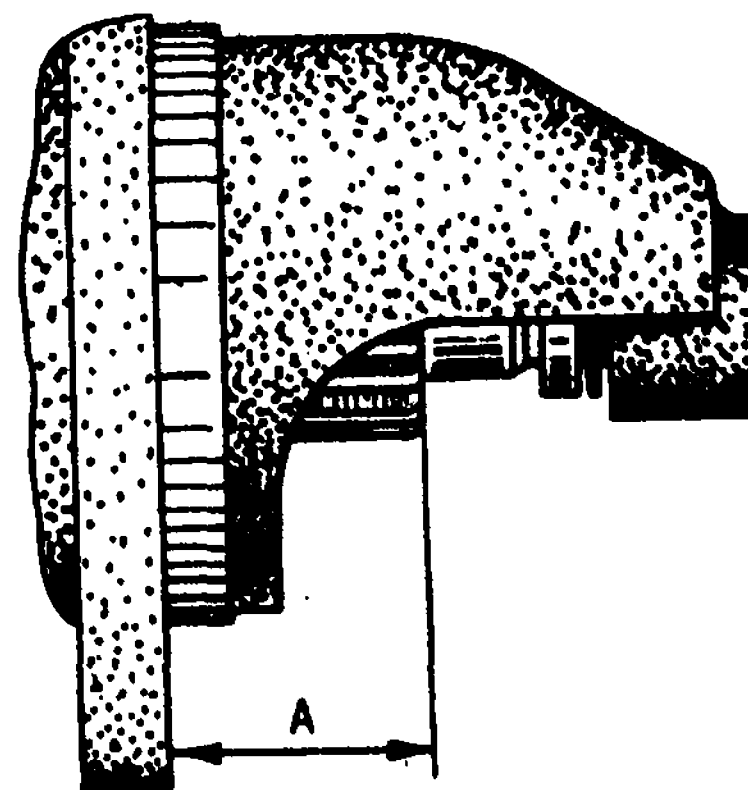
Замер положения шестерни привода в выключенном состоянии
